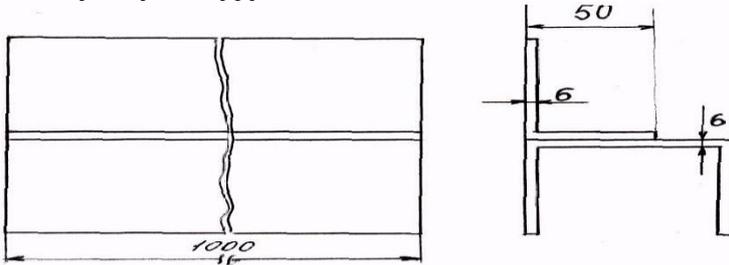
Сварная конструкция из швеллера и уголка
